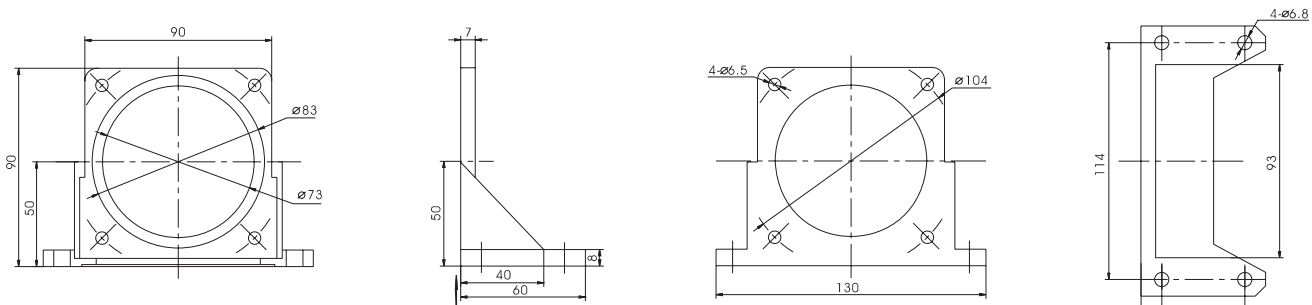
Befestigungsflansch BFM 90 | Fig. 2 : Mounting bracket BFM 90
